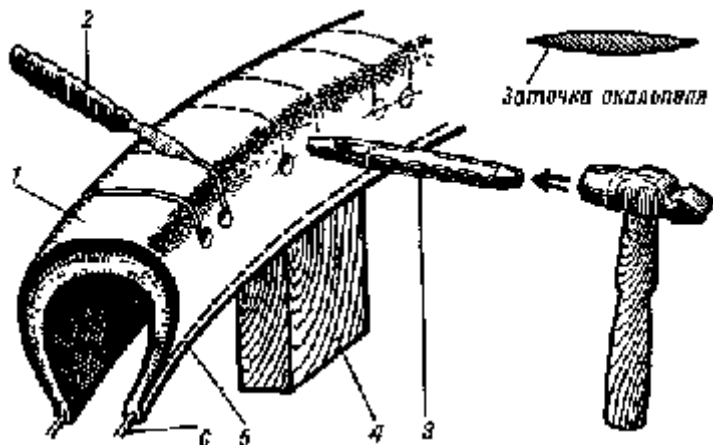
Изготовление резиновой «цепи» противоскольжения: 1 — крышка-заготовка; 2 — скальпель; 3 — пробойник; 4 — деревянная подкладка; 5 — линия обреза бортов; 6 — проволочное кольцо
